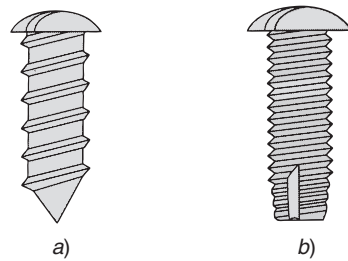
Tornillos autorroscantes a) para formado de rosca y b) para corte de rosca.
